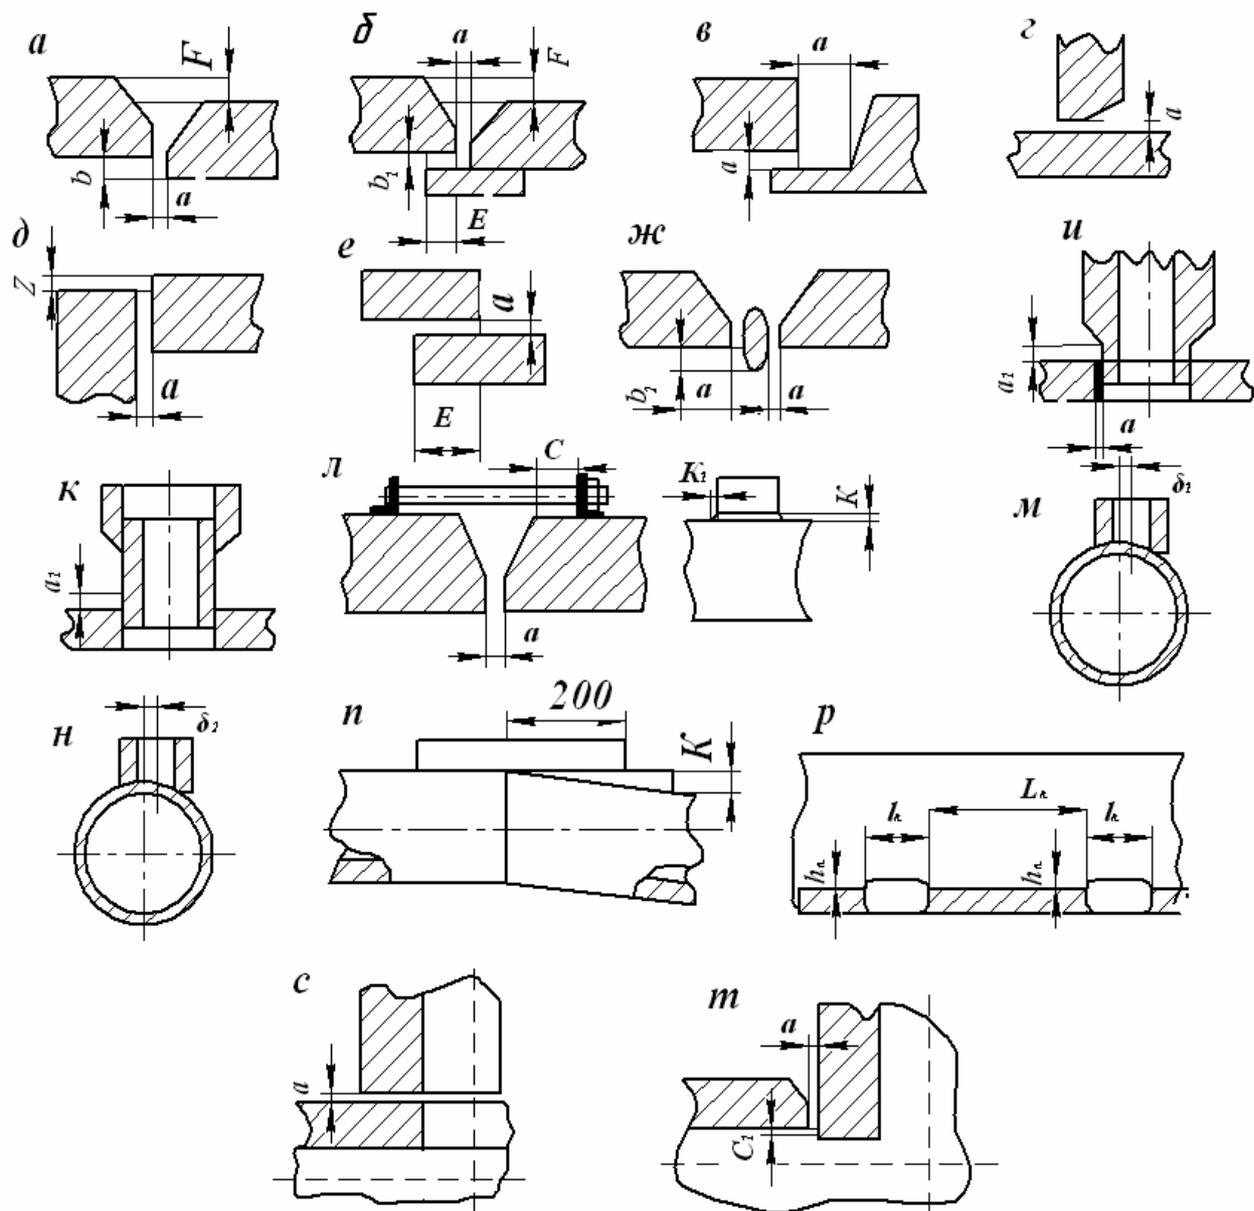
Размеры, контролируемые при сборке соединения под сварку: *a* – стыковое соединение; *б* – стыковое соединение с остающейся подкладной пластиной (кольцом); *в* – стыковое замковое соединение; *г* – тавровое соединение; *д* – угловое соединение; *е* – нахлесточное соединение; *ж* – стыковое соединение с расплавляемой вставкой; *и*, *к* – угловые соединения штуцеров; *л* – соединение с приварными элементами временных креплений; *м* – соединение с несоосностью осей штуцера и корпуса; *н* – соединение с несоосностью осей в угловых соединениях труб; *п* – соединение с переломом осей цилиндрических деталей; *р* – прихватки соединения; *с*, *т* – тройниковое (угловое) соединение
